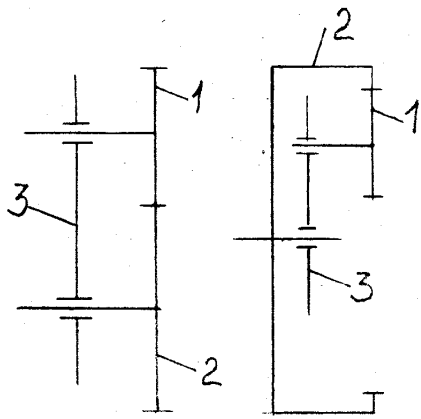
Элементарный зубчатый механизм: 1, 2 - зубчатые колеса; 3 - водило
